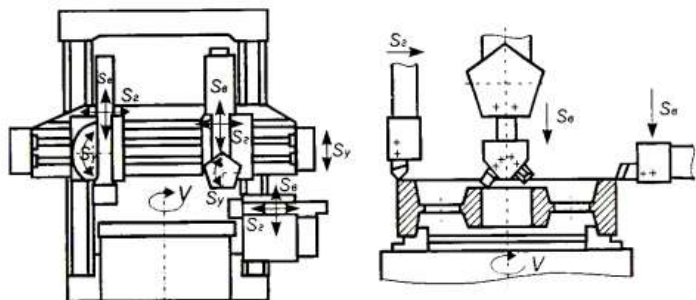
Загальний вигляд двостоякового токарно-карусельного верстата (а) і схема обробки заготовки з використанням трьох супортів (б)
